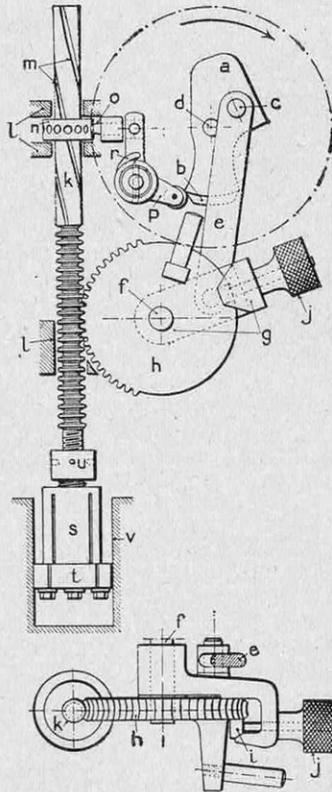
DÉTAILS DU FONCTIONNEMENT DE LA MACHINE UNIVERSELLE GUNTHER POUR RECTIFIER LES CYLINDRES ET RODER LES PISTONS
